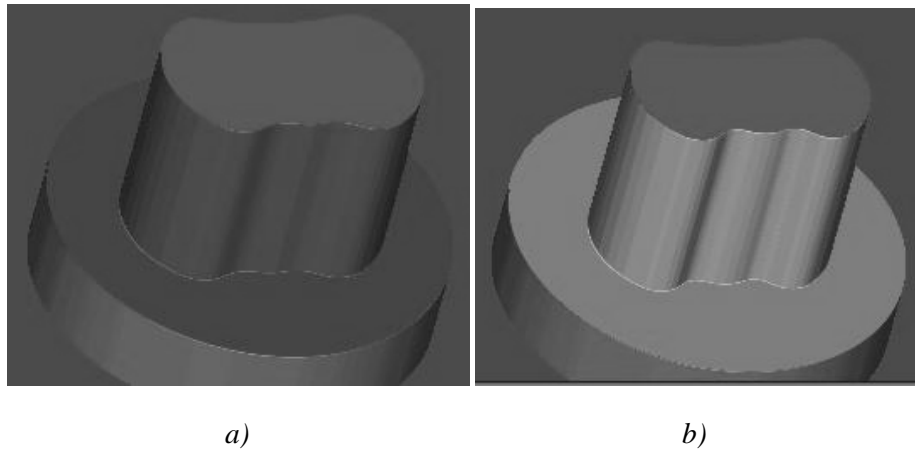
a) Punzón del destapador maquinado con cortador de 12.7 [mm]. b) Punzón del destapador maquinado con cortador de 4.76 [mm].
